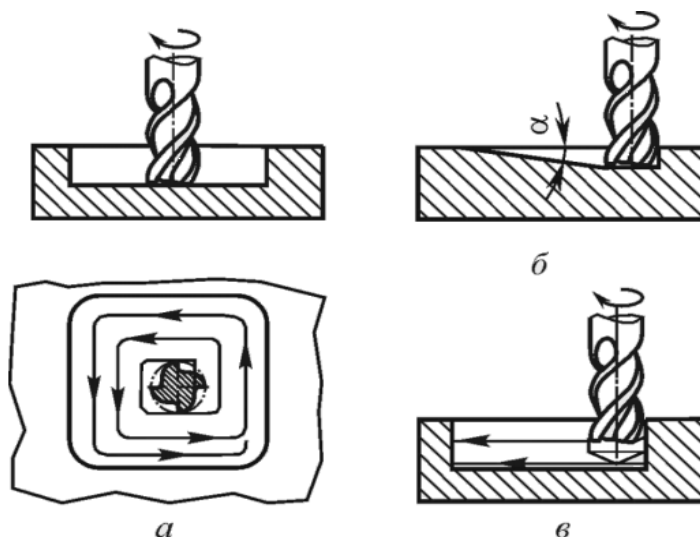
Обработка закрытых поверхностей по типовым схеме «виток» (а), врезание инструмента с подачей (б) и обработка с предварительным засверливанием (в)
